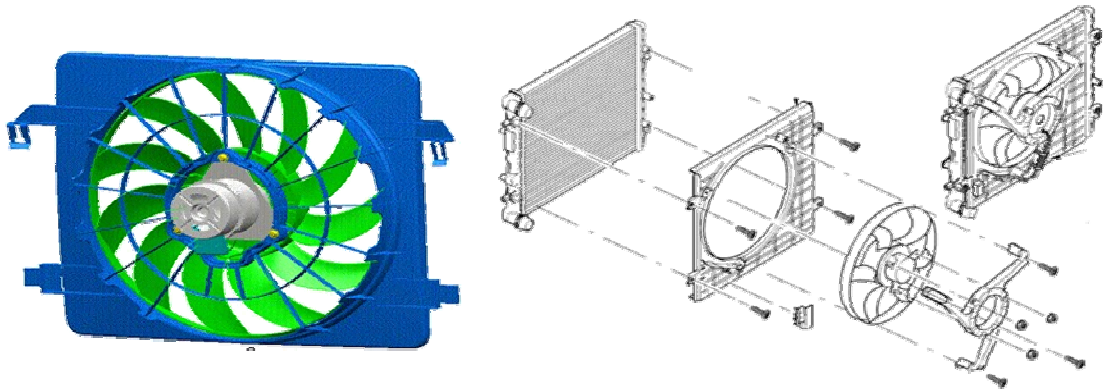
Grupo moto-ventilador: visão de conjunto e vista explodida
